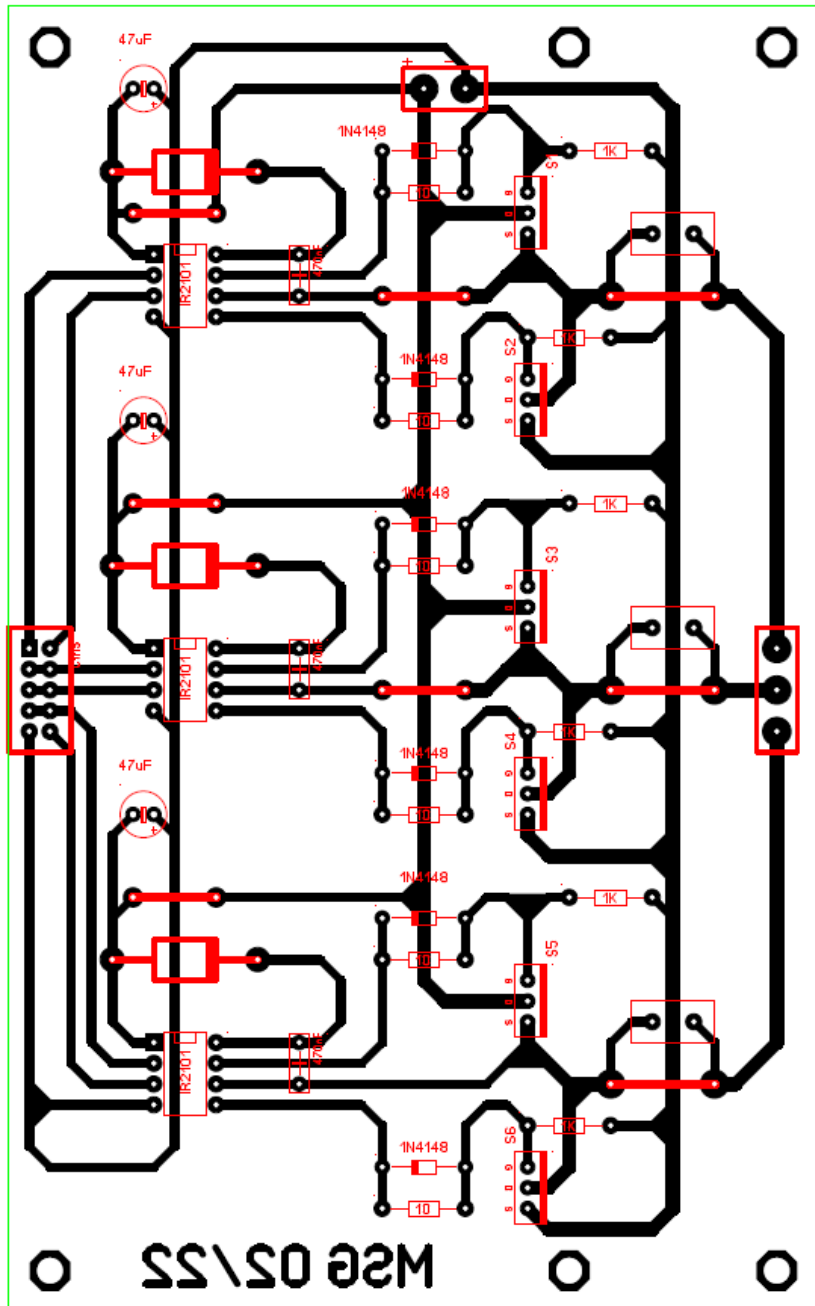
Diseño CAD de la PCB de potencia. Fuente [Propia]
